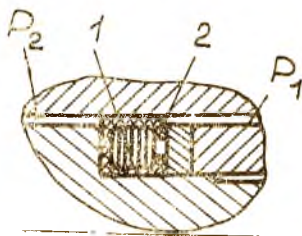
Конструкция вторичного уплотнения из материала МР и эластичной оболочки
